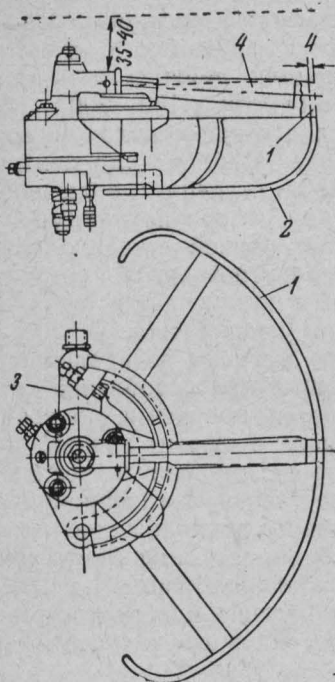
Предохранительная дуга для пневматического пускового устройства
